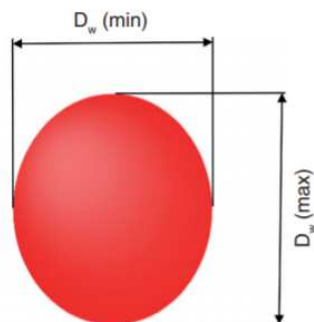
Rozměrové tolerance dotyku od firmy Renishaw [27]
